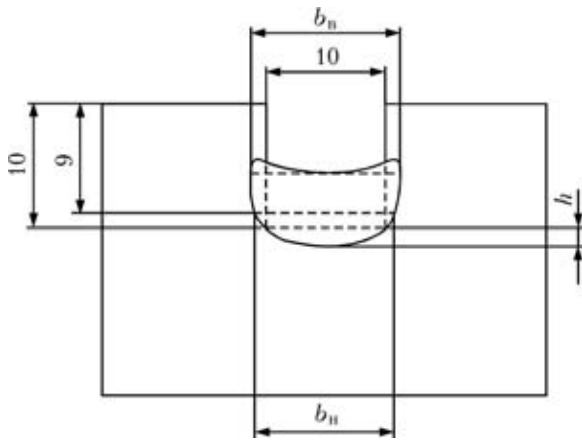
Схема наплавки валика в узкий зазор:  $h$  — глубина проплавления основного металла;  $b_в$ ,  $b_н$  — ширина валика соответственно в верхней и нижней части
